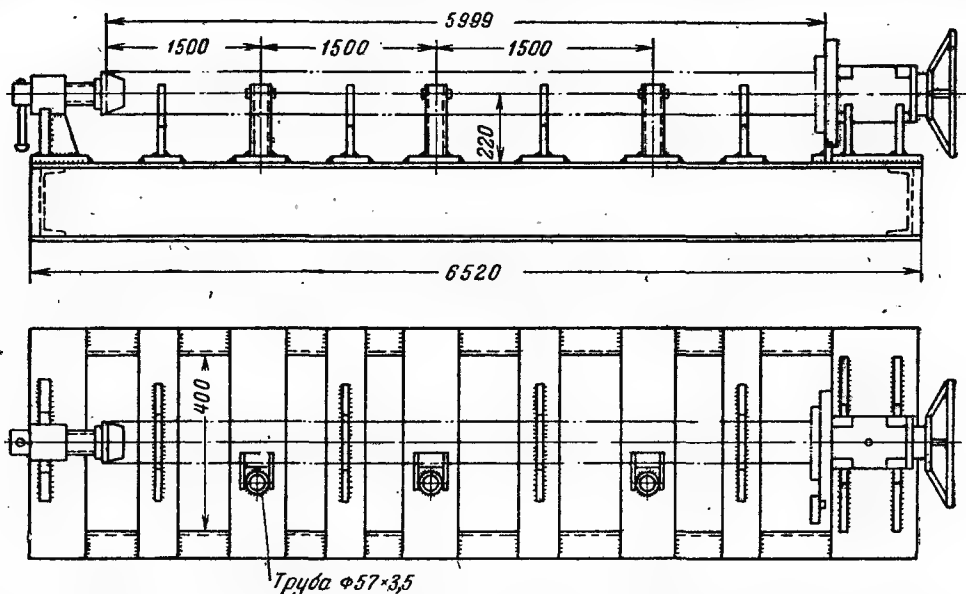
Стенд для предварительной сборки деталей теплообменника «труба в трубе».
